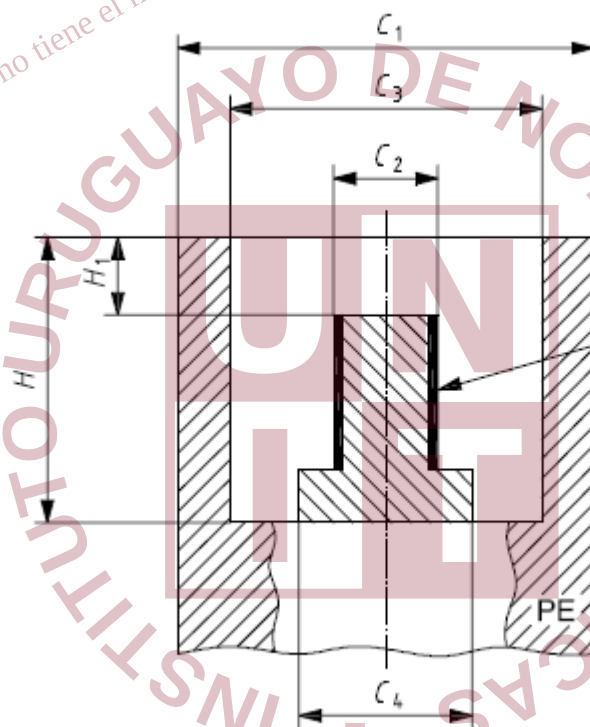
Embocadura y tubo. Símbolos para las dimensiones
